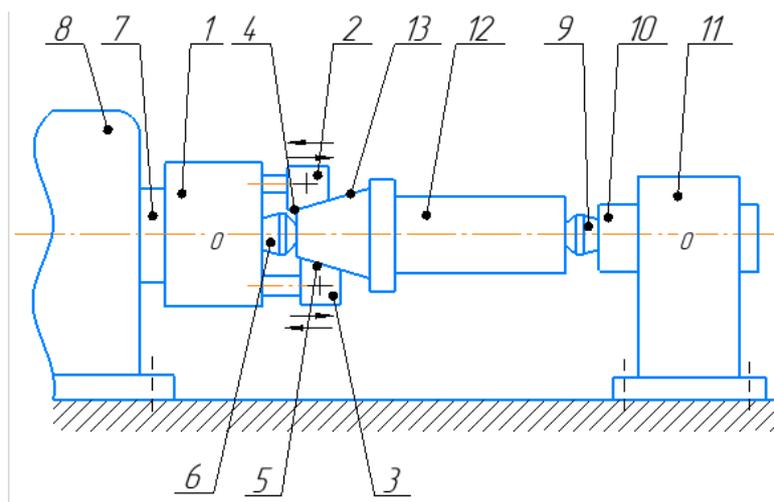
Схема способа установки вала с конической поверхностью на центрах станка
